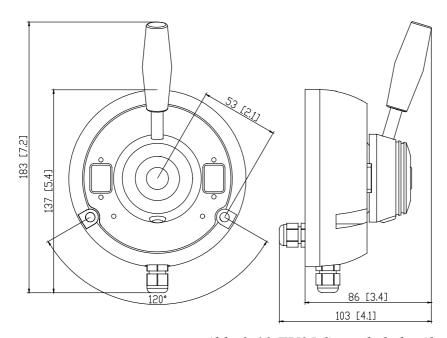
FU25 Steuerhebel - Abmessungen
